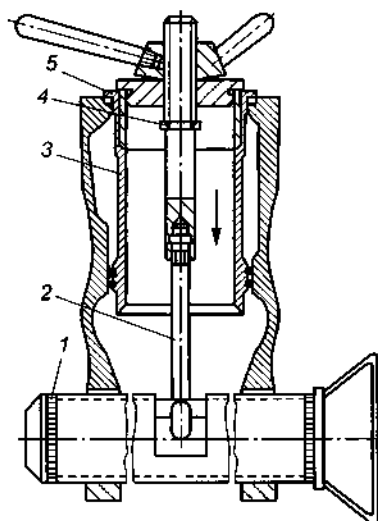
Приспособление для запрессовки гильзы в блок цилиндров: 1 — скалка; 2 — захват; 3 — гильза; 4 — упорное кольцо; 5 — оправка
